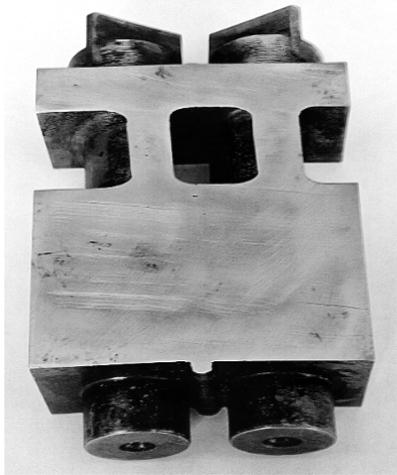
Пакет лопаток после сварки, термической и механической обработки
